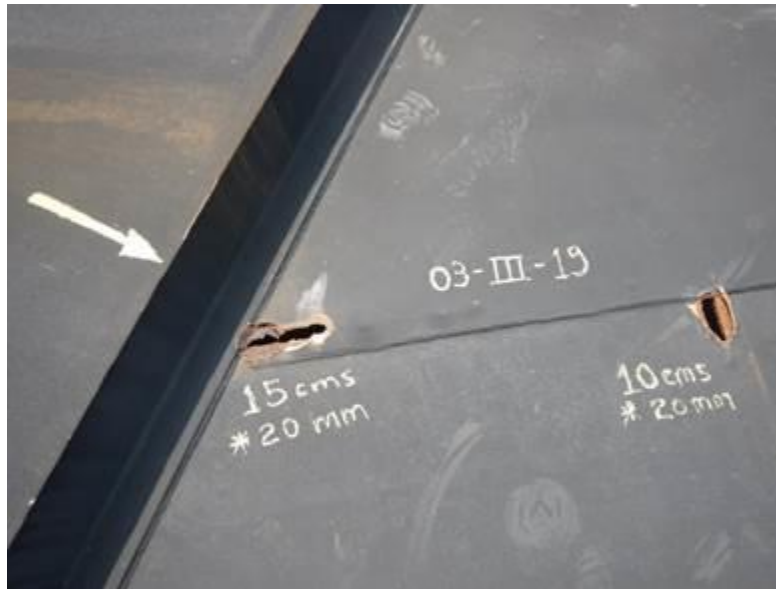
Corrosión pasante junto a la soldadura de traslape de las láminas.
